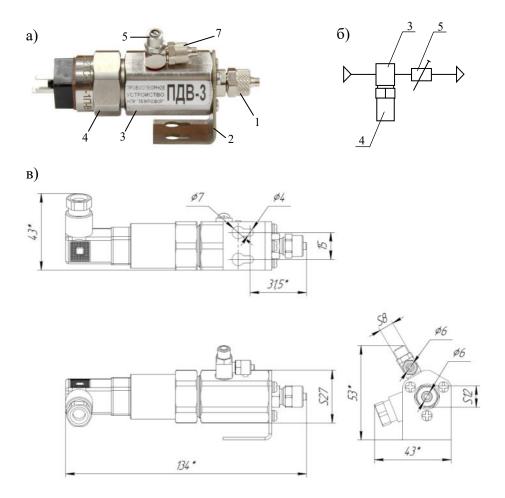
a) внешний вид, б) принципиальная пневматическая схема, в) габаритные размеры ПДВ-3-Б
